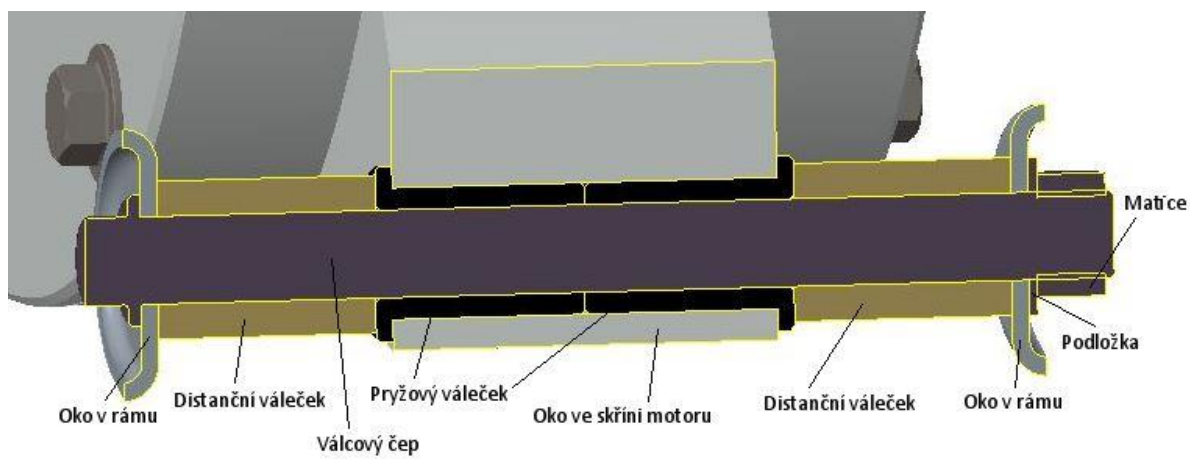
Přípojná místa vytvořená na skříni motoru
